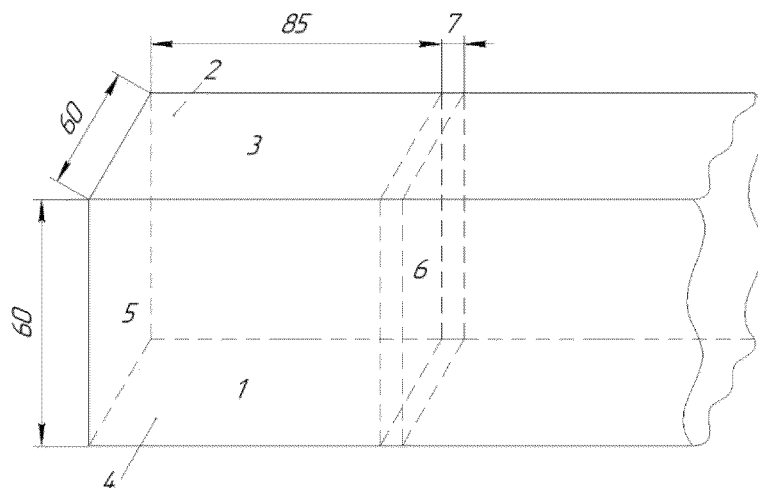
Спосіб отримання штучних заготовок з прокату сортового сталевих гарячекатаного квадратного
